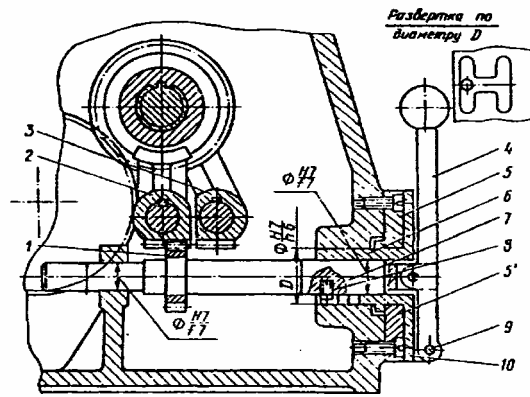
Однорукаютное управление двумя блоками зубчатых колес
